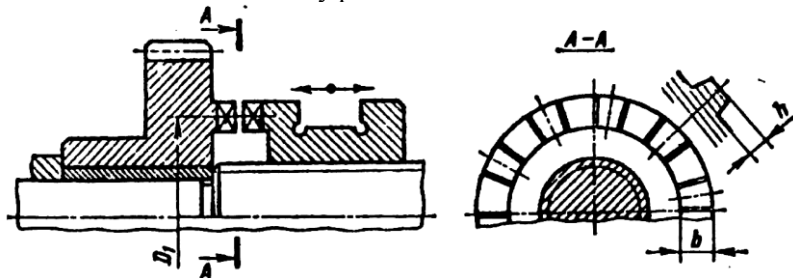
Принципова конструкційна схема кулачкової муфти
